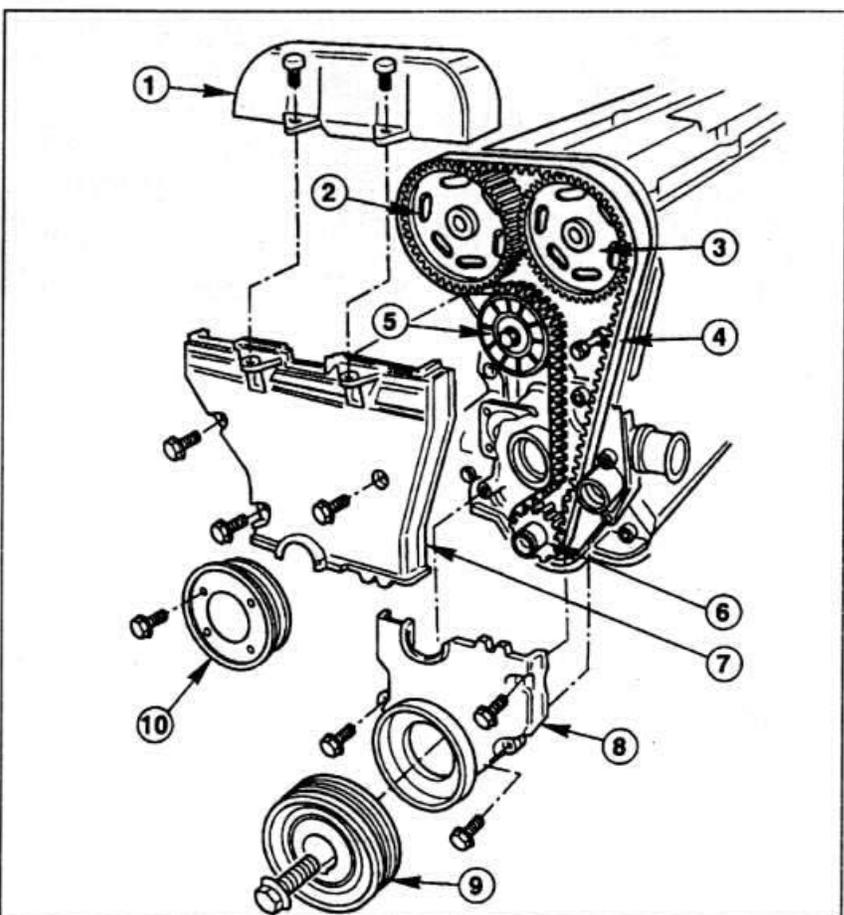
С.9. Зубчатый ремень и крышки зубчатого ремня.
